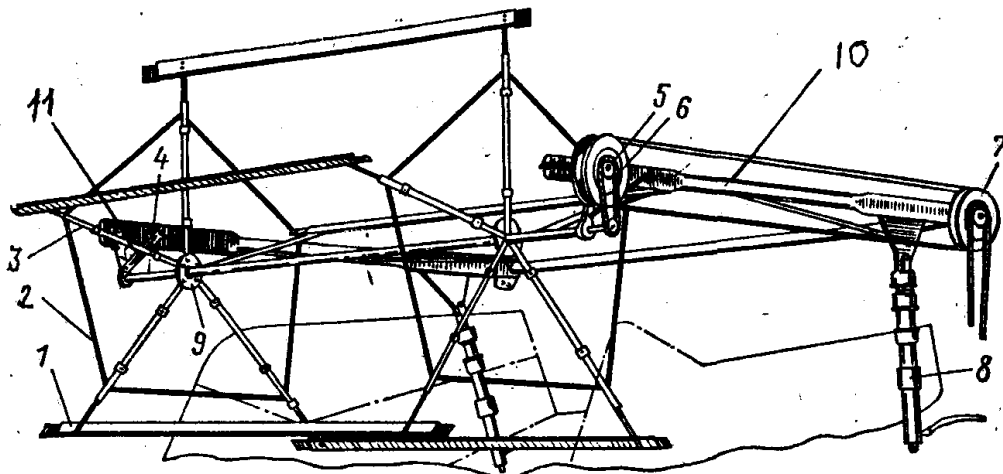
Мотовила комбайна КС-1,8 «Вихрь»: 1 – планка; 2 – стяжка; 3 – луч; 4 – вал; 5 – цепная передача; 6 и 7 – шкивы; 8 – гидроцилиндр; 9 – диск; 10 – поддержка; 11 – подвеска
